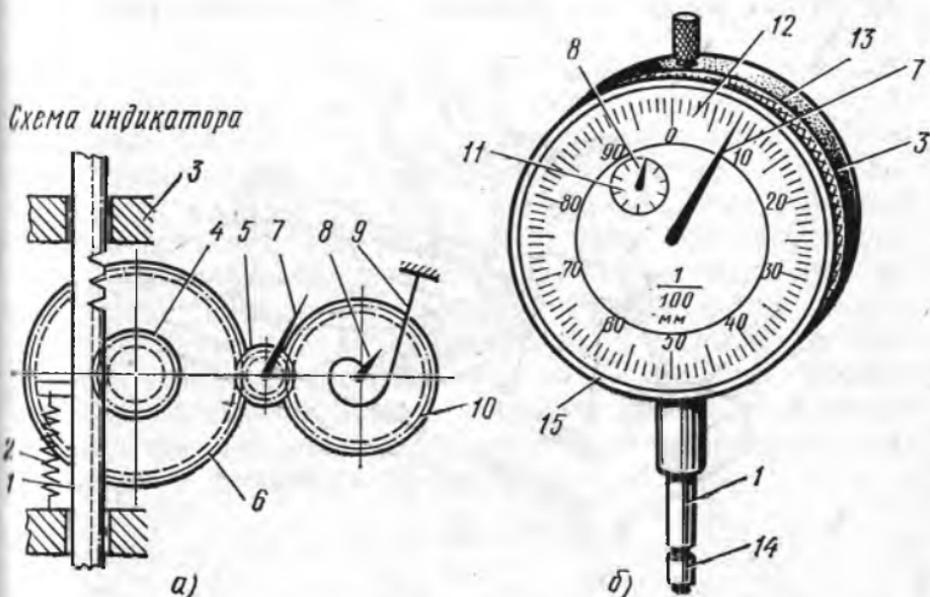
Схема (а) и общий вид (б) индикатора часового механизма:
